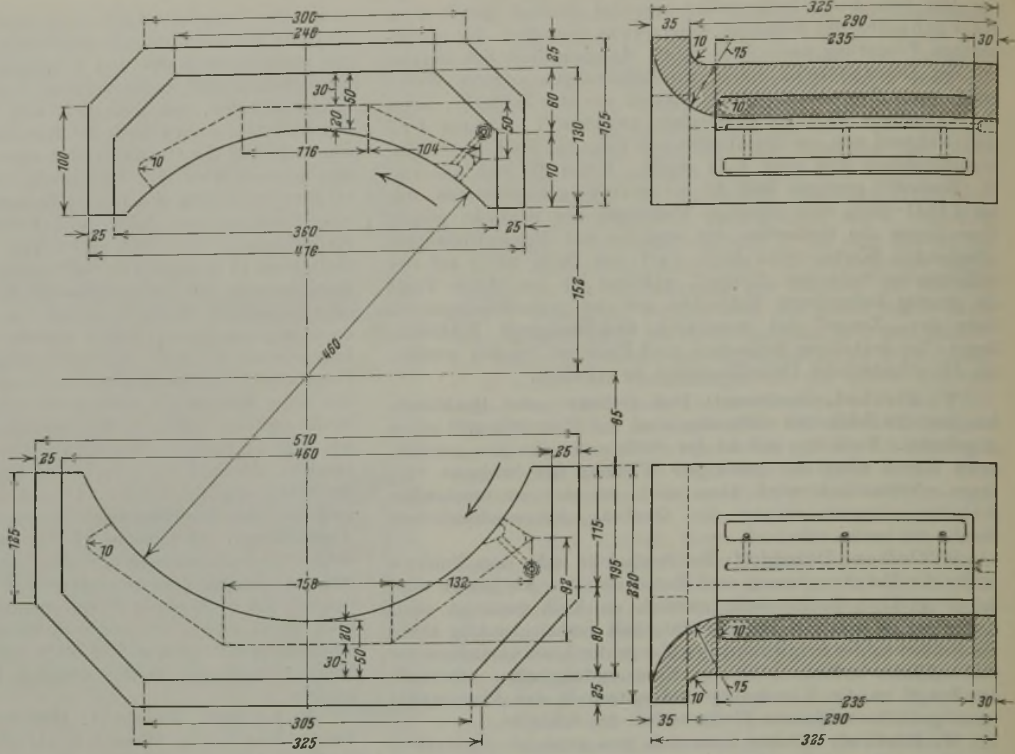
Neue Lagerbauart für ein Zweiwalzen-Metallwarmwalzgerüst.
